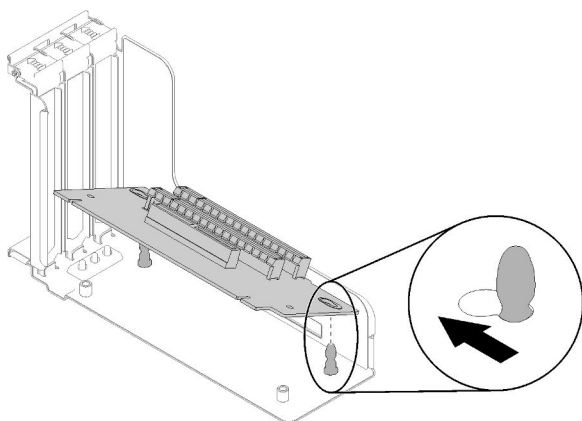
Desensamblaje del conjunto de tarjeta de expansión PCIe
